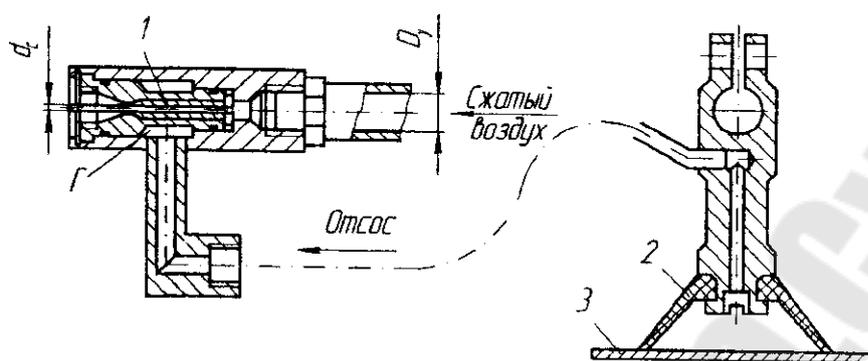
Схема работы вакуумного захвата с эжектором: 1 – сопло эжектора, 2 – присос, 3 - заготовка
